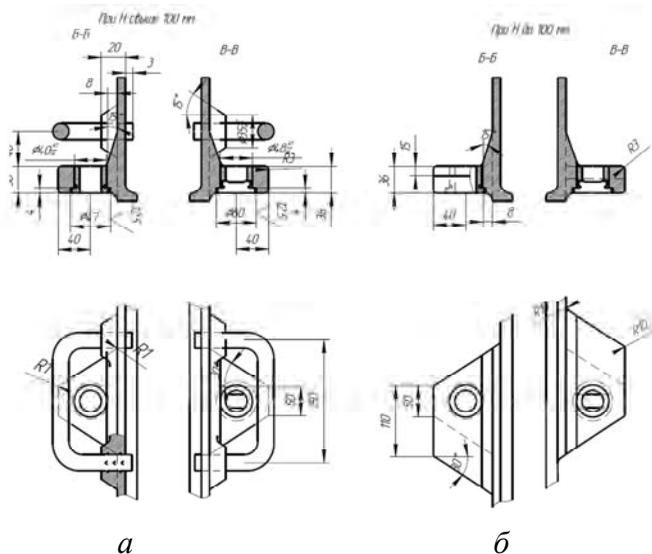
Конструкции приливов для установки центрирующей и направляющей втулок и элементов транспортировки опок:
